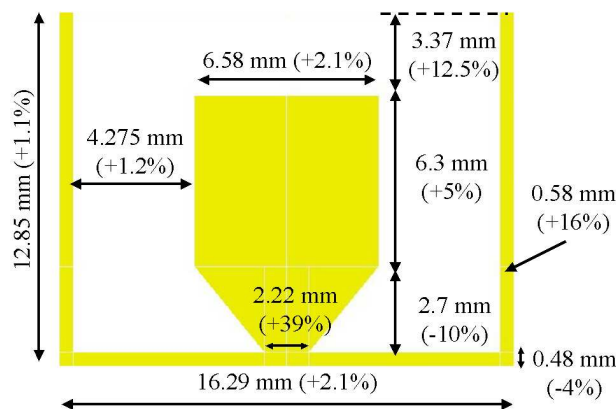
Relevé des dimensions du premier prototype après découpe et écart en pourcentage avec les dimensions théoriques.
